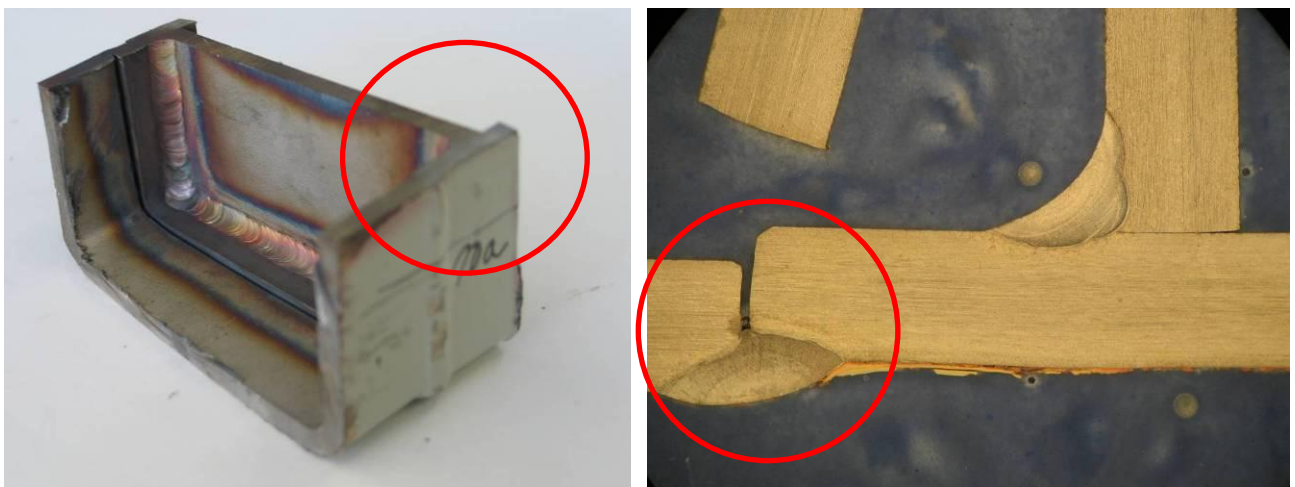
Ausgeführte Schweißung Vierkantrrohr - rechte Seite dazugehöriges Schlibbild
